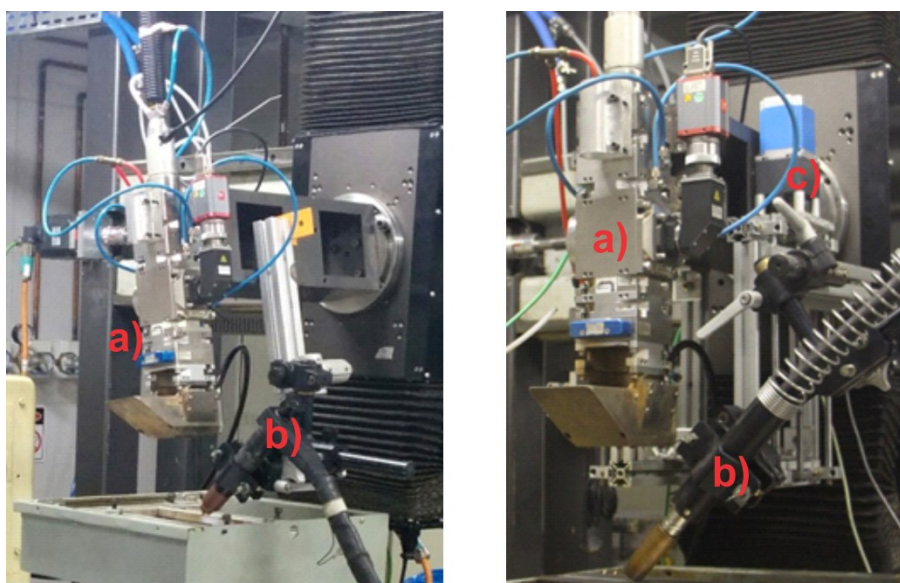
Bancada de trabalho de soldagem HLAW (esquerda) antes e (direita) depois do desenvolvimento do Sistema de Movimentação do Suporte Orientador (SMS) acoplado à tocha de soldagem GMAW. a) Cabeçote de soldagem LBW, b) Tocha de Soldagem a Arco, c) Sistema de Movimentação do Suporte Orientador. (Fonte: Autor)
